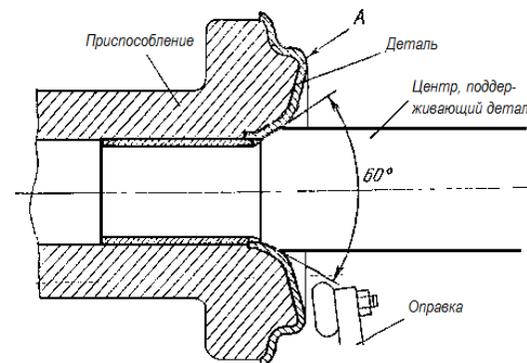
Схема правки крышки корпуса молочного насоса НМУ-6
